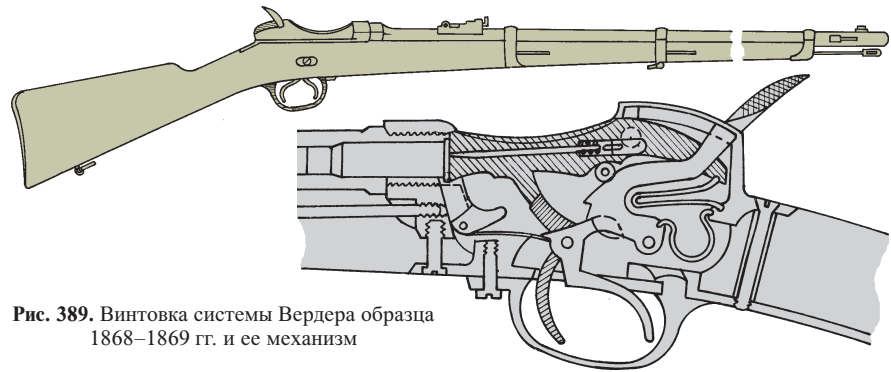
Винтовка системы Вердера образца 1868–1869 гг. и ее механизм
